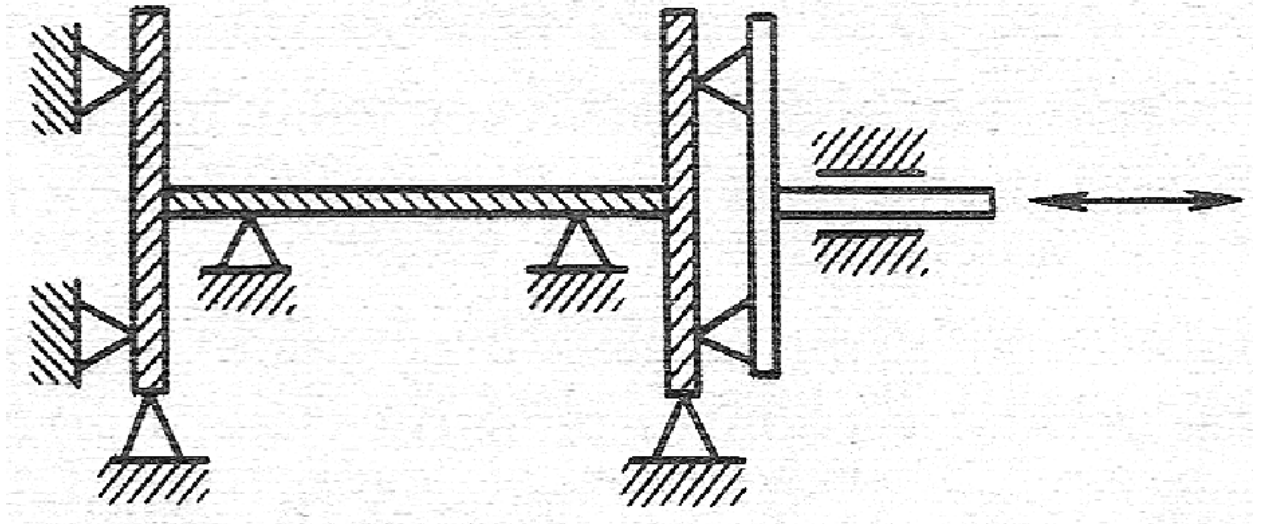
Схема базування двотаврової балки заготовки
